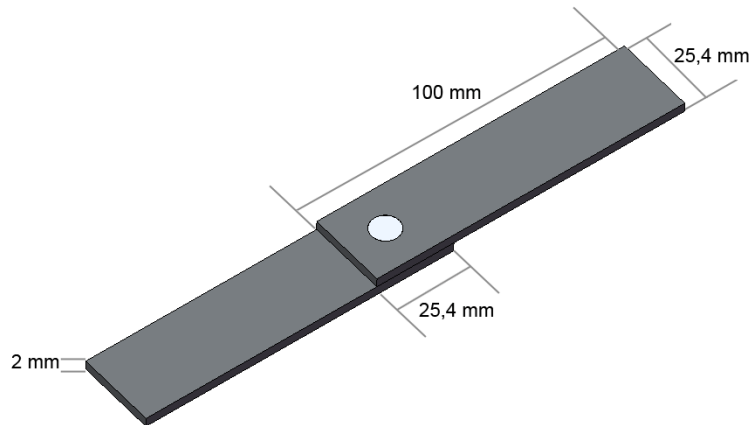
Geometria da amostra de PMMA soldada por FSSW.
